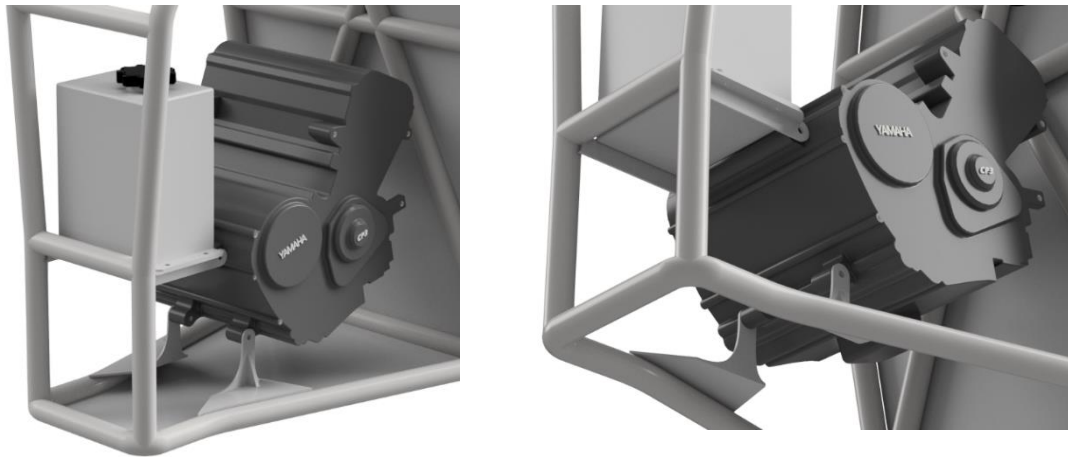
Soportes posteriores (izquierda) e inferiores (derecha) del conjunto motor - depósito
